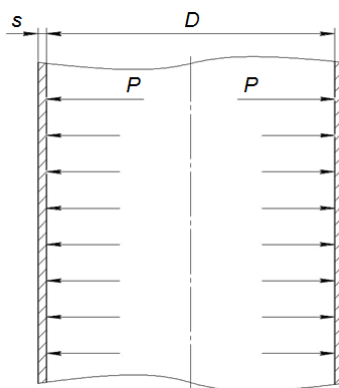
Схема до розрахунку товщини стінки циліндричної обичайки
